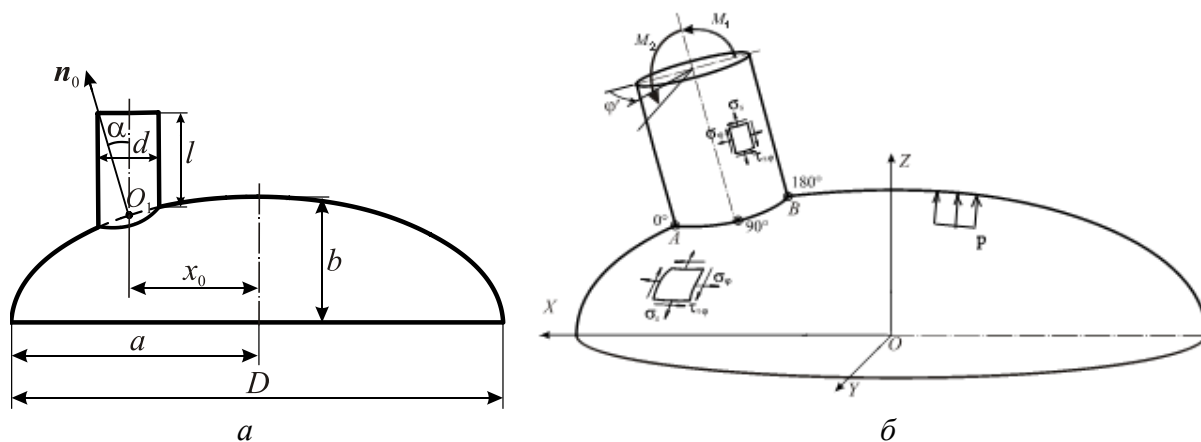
Эллипсоидальное днище с патрубком: а – геометрия соединения; б – нагрузка и напряжения
